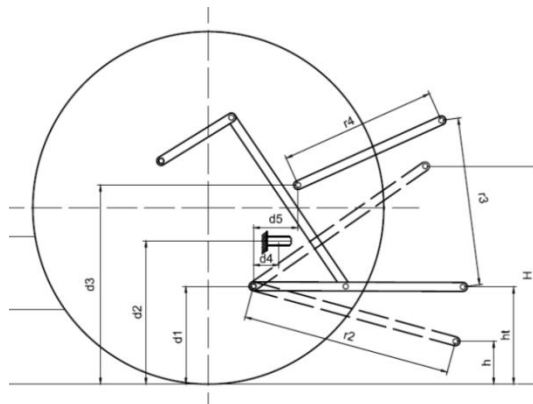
Dimensiones del sistema de levante de un tractor agrícola.
